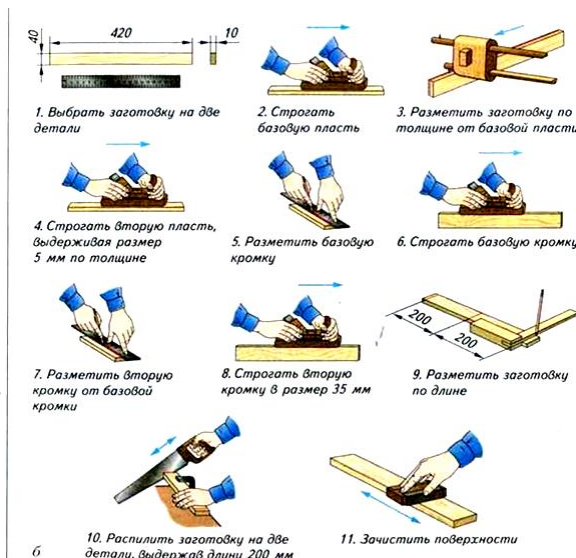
Изготовление планки для декоративной подставки под горячую посуду: а – чертёж; б – технологический процесс (1 – 11)
